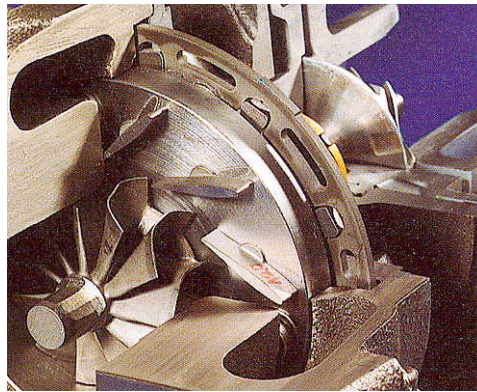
Turbolader mit verstellbarer Turbinengeometrie (VTG)
